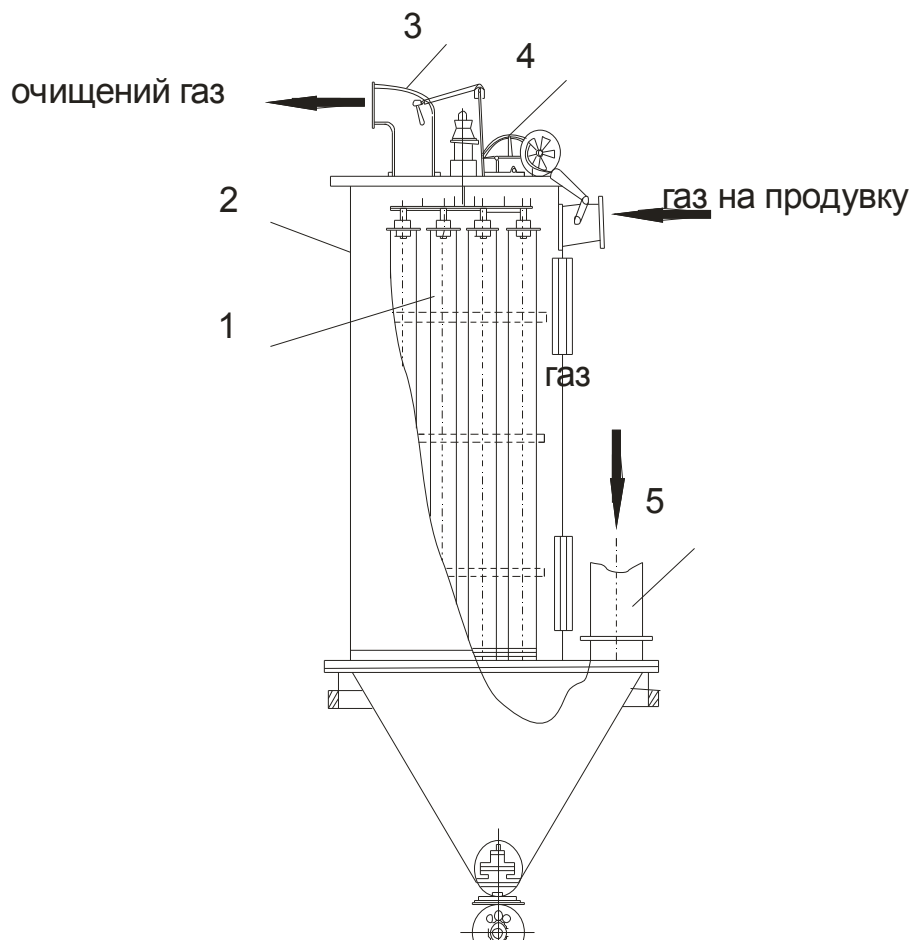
Рукавний фільтр: 1 – рукав; 2 – корпус; 3 – вихідний патрубок; 4 – пристрій для регенерації; 5 – вхідний патрубок.
